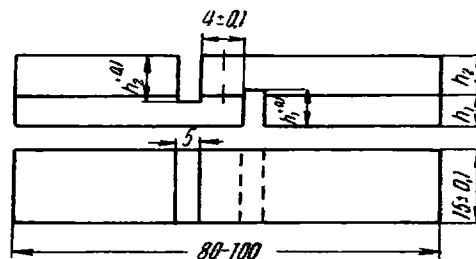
Образцы для испытания прочности сцепления на срез компонентов биметалла
